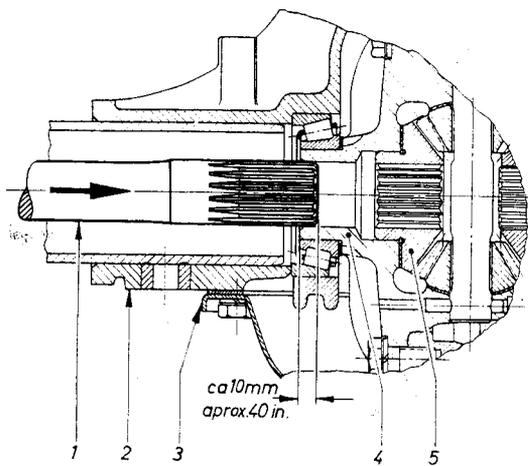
Hinterachswelle in Bohrung des Ausgleichgehäuses eingeführt
